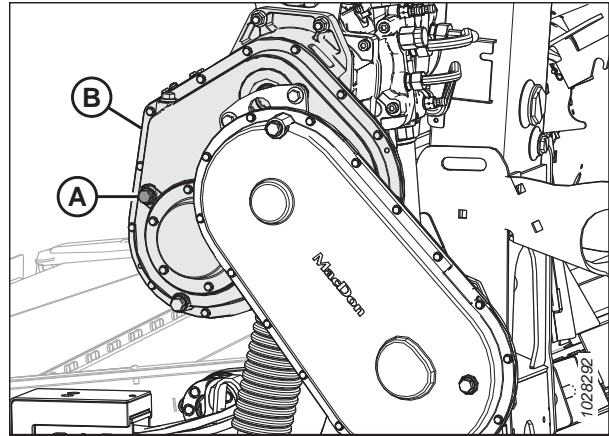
Schneidwerk-Hauptgetriebe
